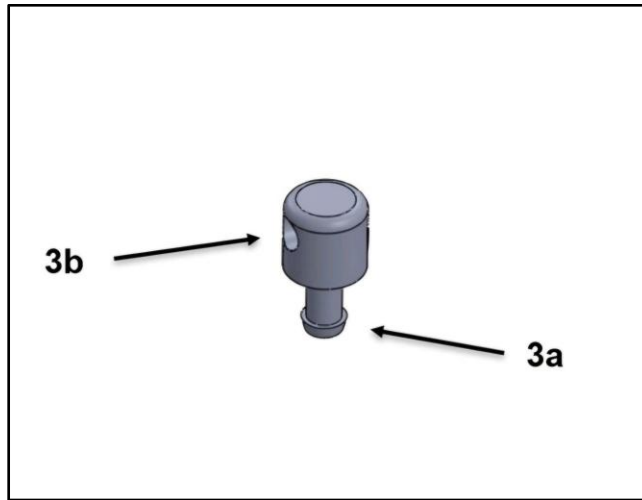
Pino destorcedor com ponta facetada e furo passante para fixação
